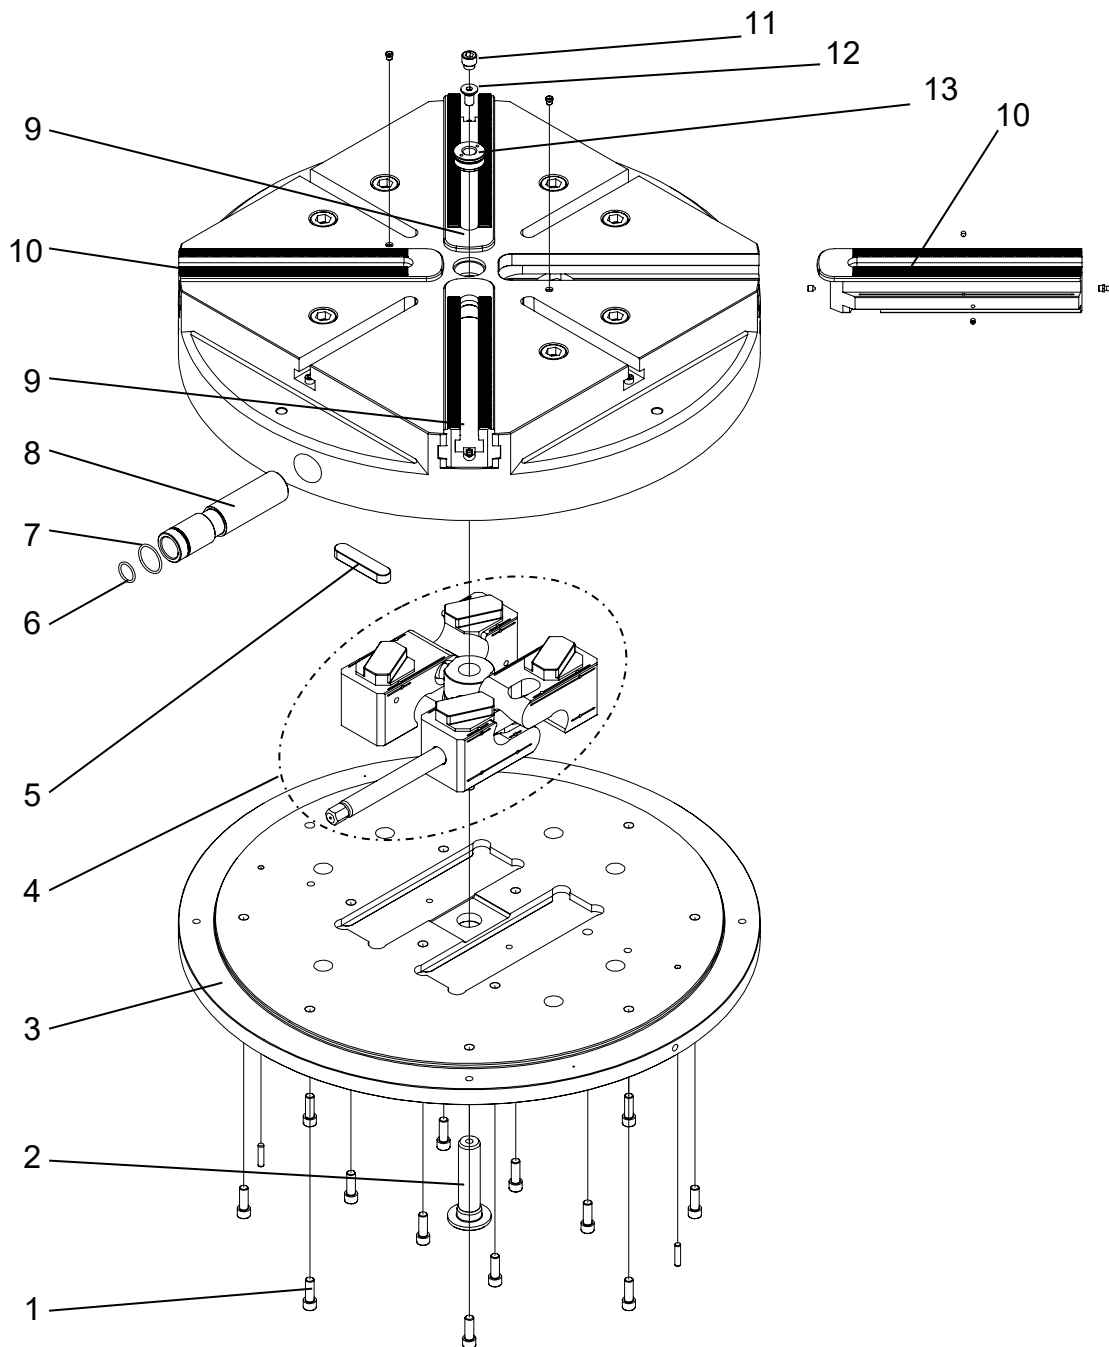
Desmontaje/montaje del mandril de sujeción (VD080)
